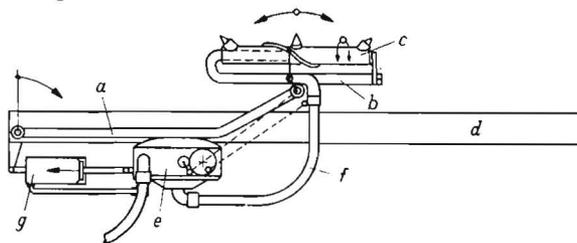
Kardantartig geführtes Düsenrohr für die Unterwäsche; a Schwenkarm, b Düsenrohrhalter, c Düsenrohr, d Rost, e Regner-turbine, f Hochdruckschlauch, g Hydraulik-Zylinder
